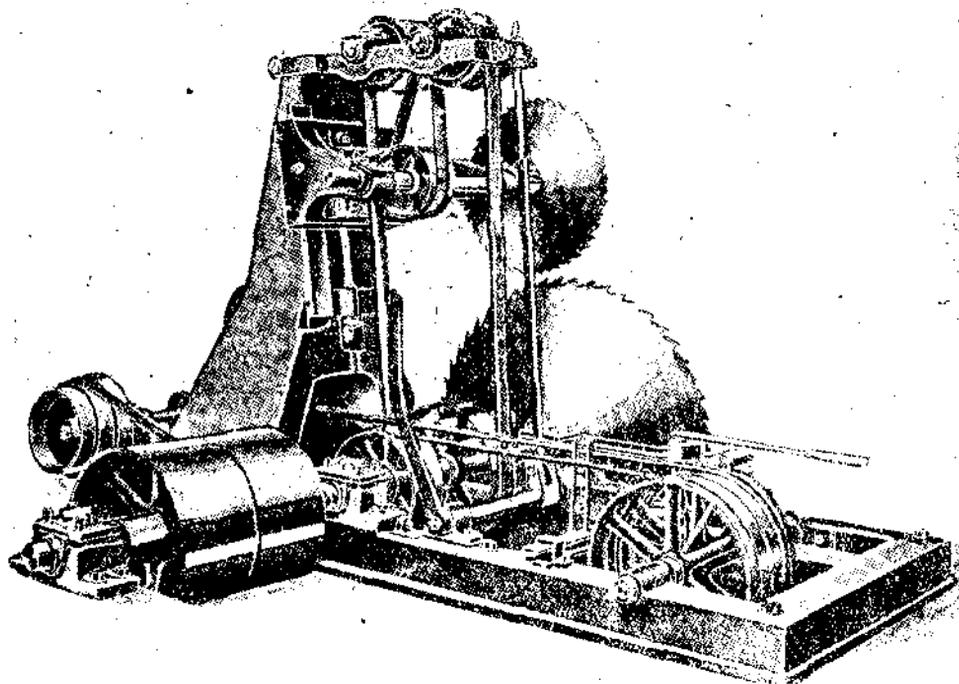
Лесопильный станок с двумя круглыми пилами.
